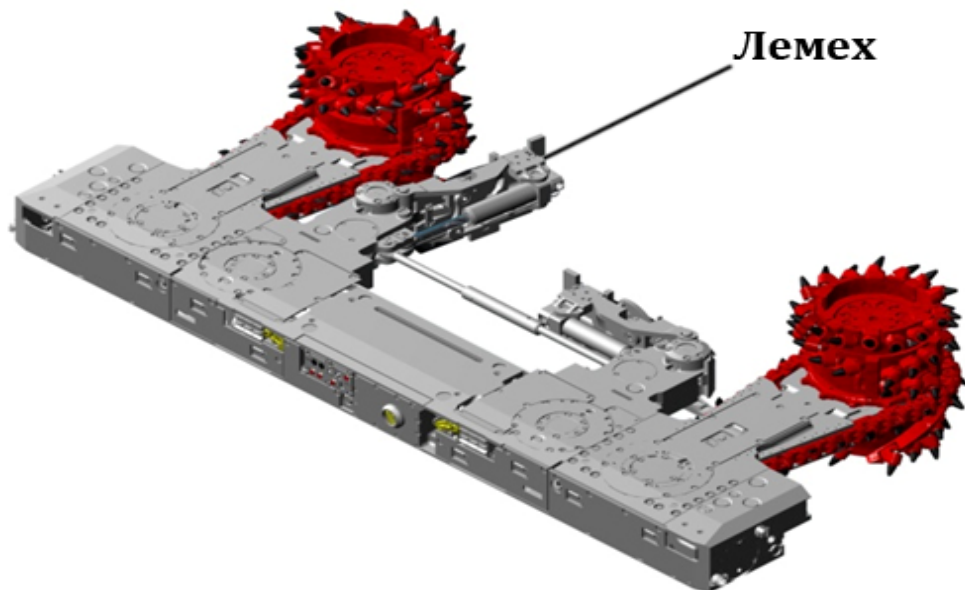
Схема установки лемеха на комбайне КА-200 с барабанными исполнительными органами
